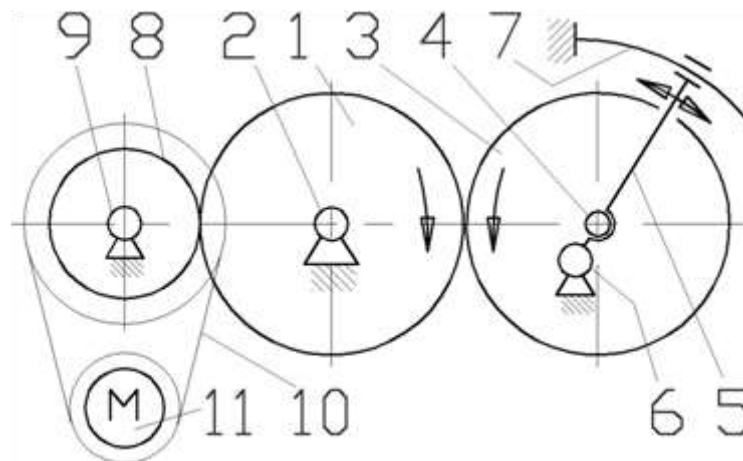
Схема установчого механізму плющильного верстата.
